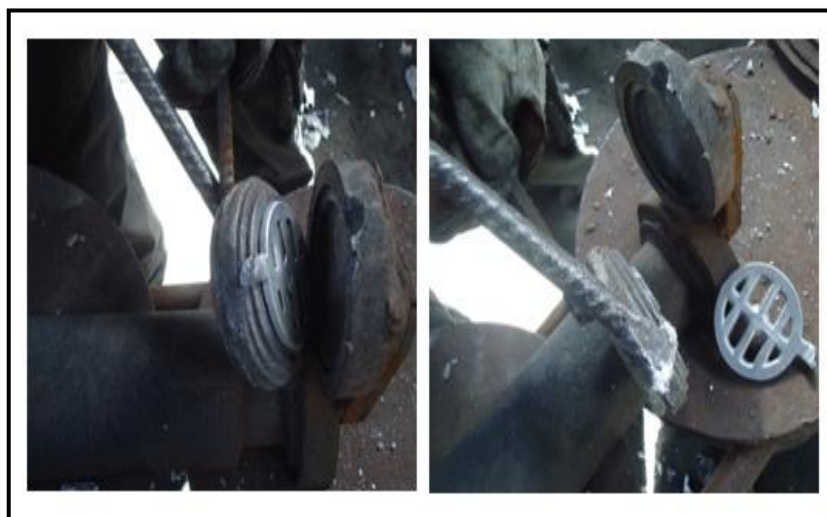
Montaje de hembra y macho de la tapa y su colado.
